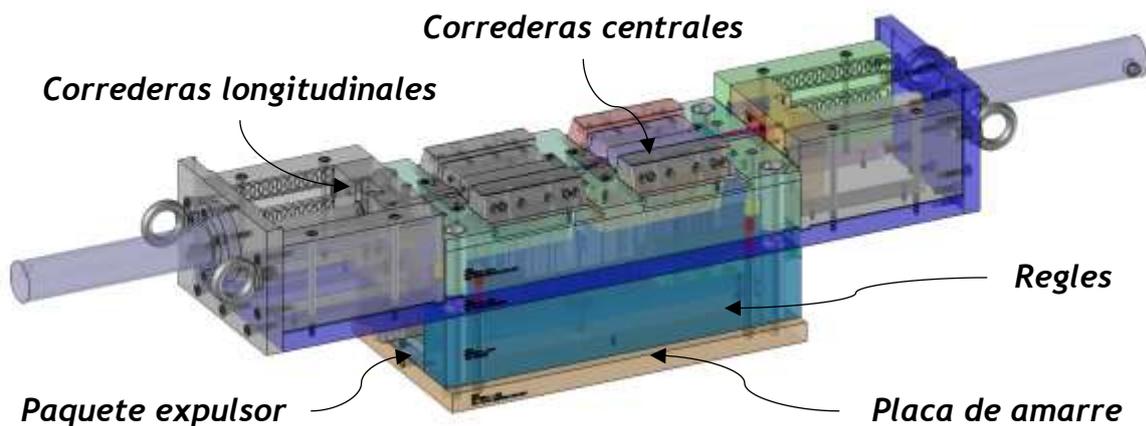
Vista trimétrica del lado de la expulsión del molde.
